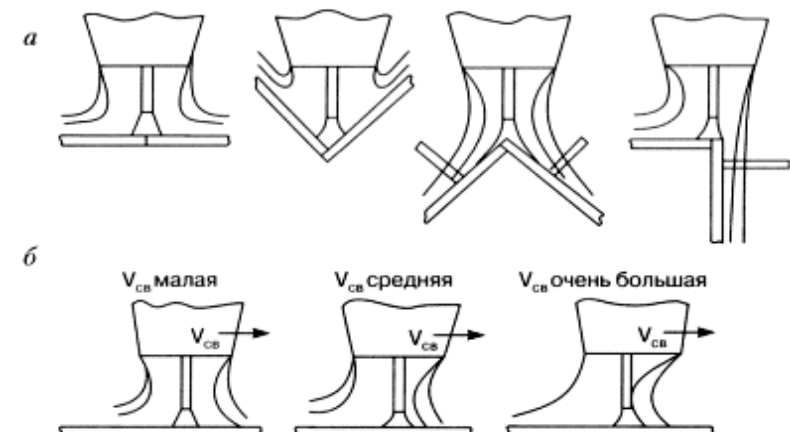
Влияние типа сварочного соединения (а) и скорость сварки (б) на эффективность газовой защиты[21].
